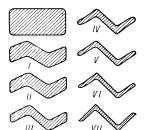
Схема изменения сечения (калибровка) при прокатке зетового профиля.
